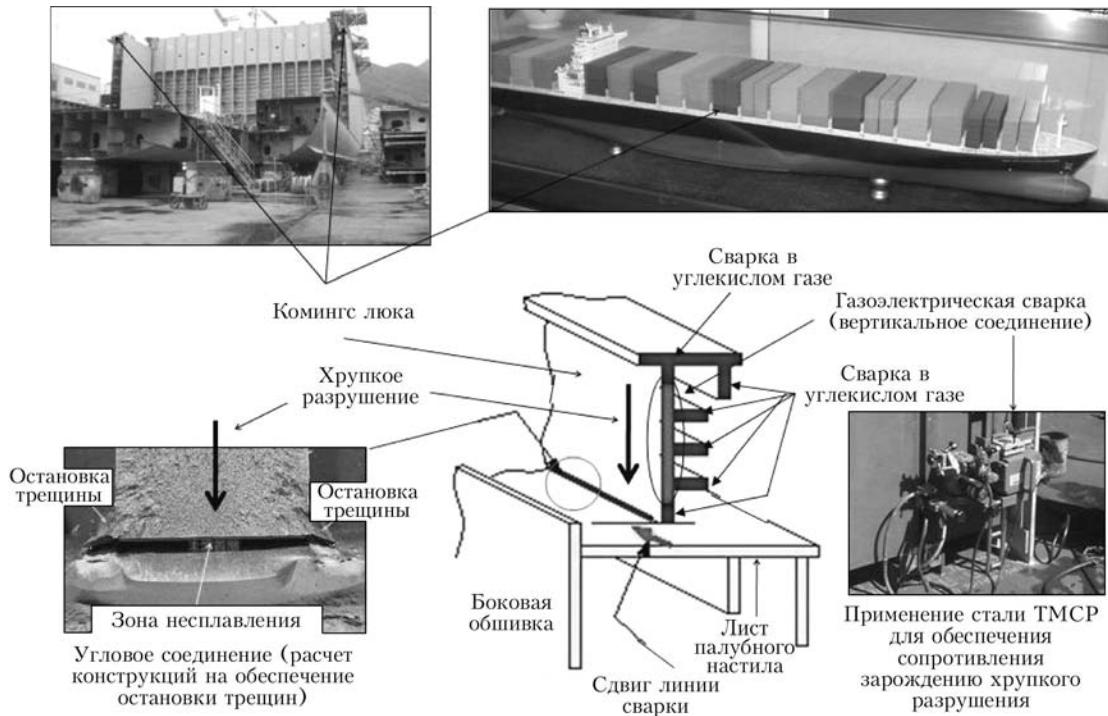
Конструкция контейнеровоза и концепция обеспечения безопасности сварных соединений на комингсах люка с помощью расчета сопротивления хрупкому разрушению
